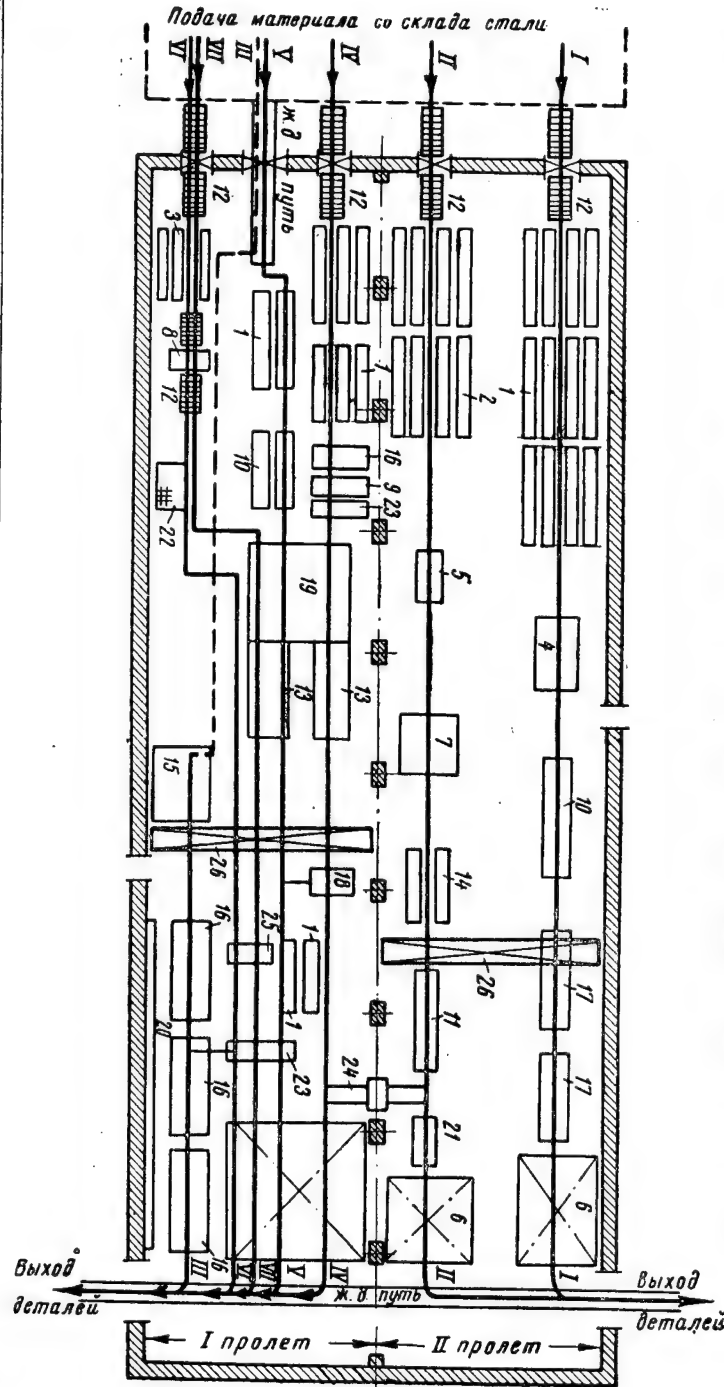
Схематическая планировка корпусообработывающего цеха:
